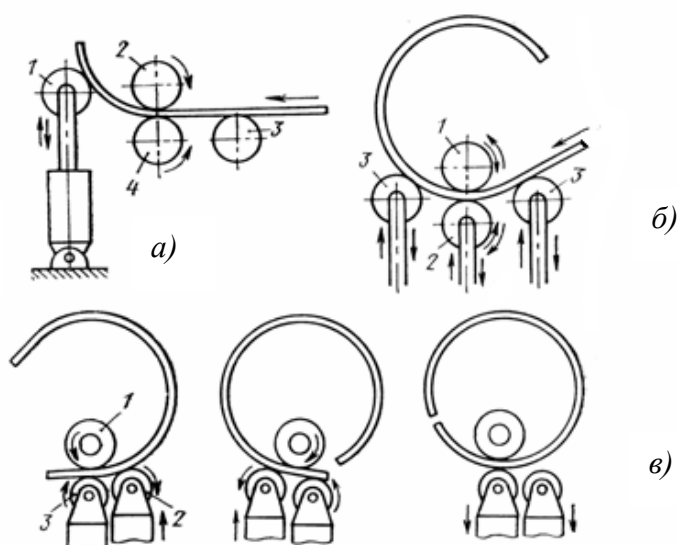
Схема гибки на профилегибочных станках: а – станок ПГ-2м (1 – гибочный ролик; 2 – верхний приводной ролик; 3 – направляющий ролик; 4 – нижний приводной ролик); б – станки ПГ-3 и ПГ-4 (1 – верхний приводной ролик; 2 – нижний приводной ролик; 3 – гибочные ролики); в – станок ПГ-6 (1 – верхний ролик; 2 и 3 – нижние ролики)
